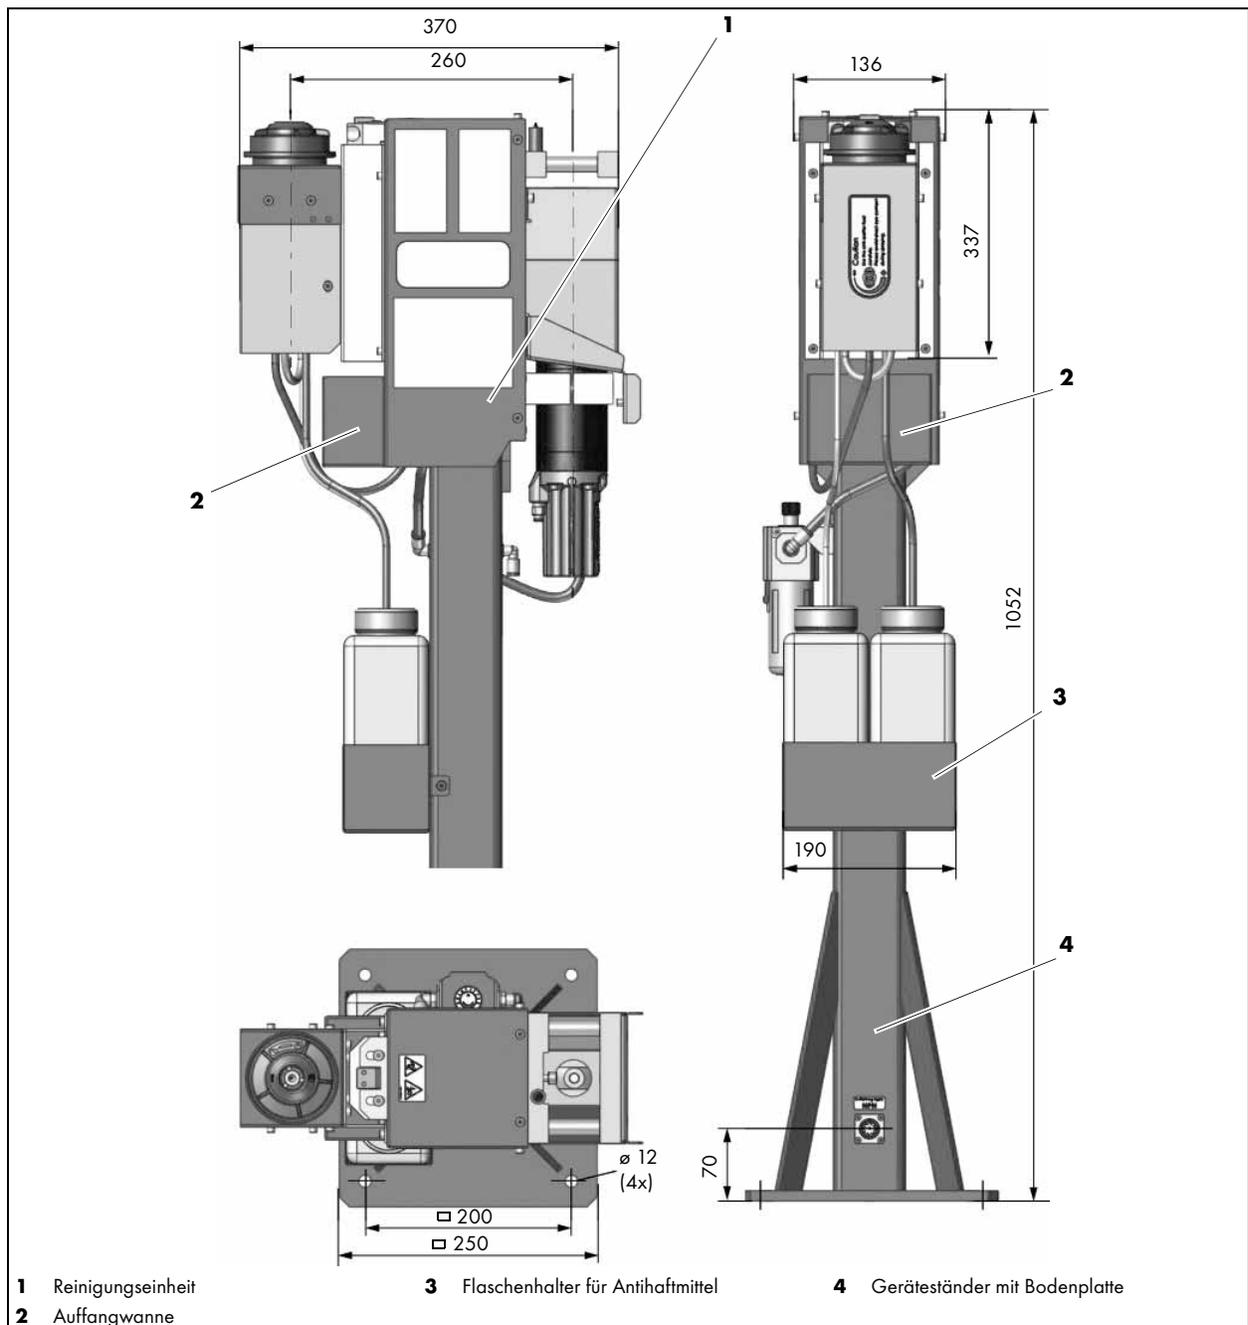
Technische Daten - Ausführung mit langem Geräteständer
